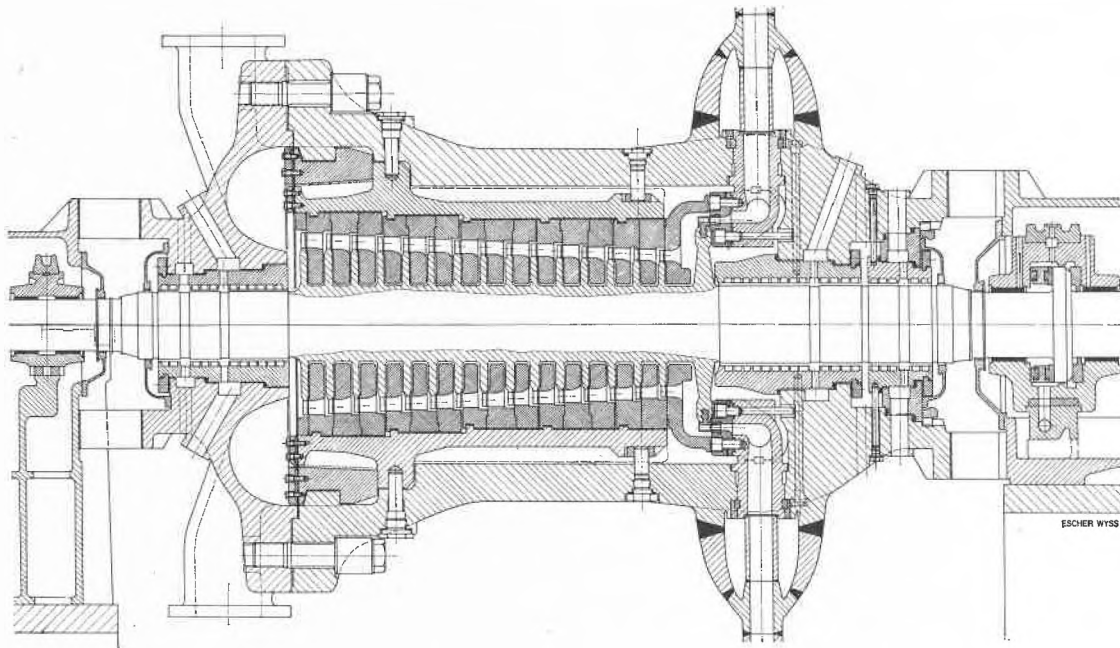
Längsschnitt durch eine HD-Dampfturbine für 250 an Frischdampfdruck in sogenannter Topfbauart, d. h. ohne horizontalen Teilflansch
